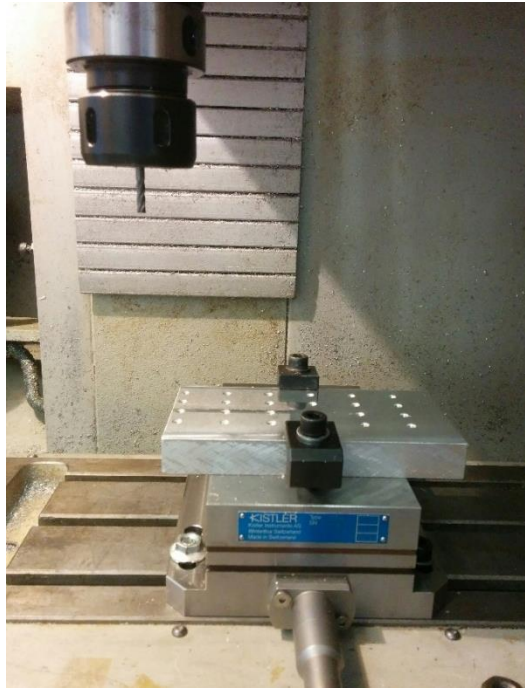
Disposición de pieza y fresa de 4 mm para el ensayo en Odisea.
